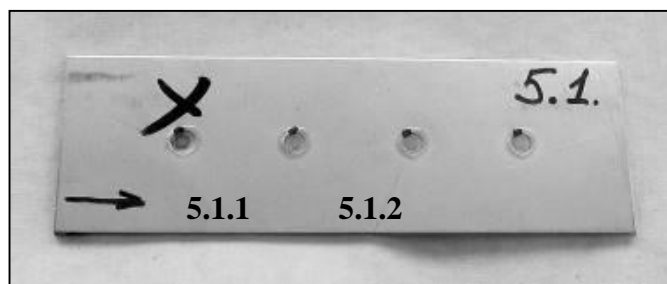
Внешний вид точечной контактной сварки образца № 5.1
